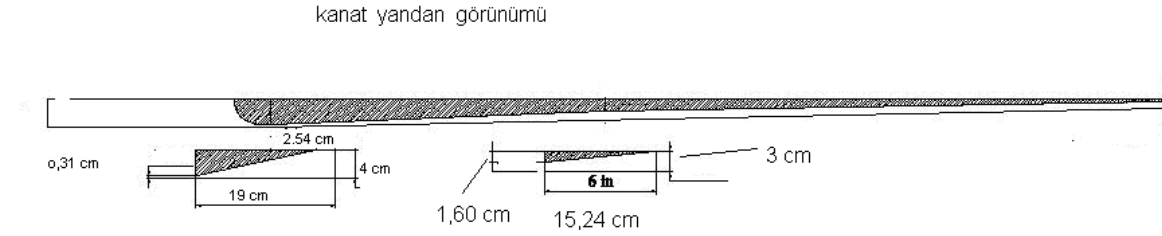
Türbin Kanadının Rotor mili Bağlantı kısmı.
